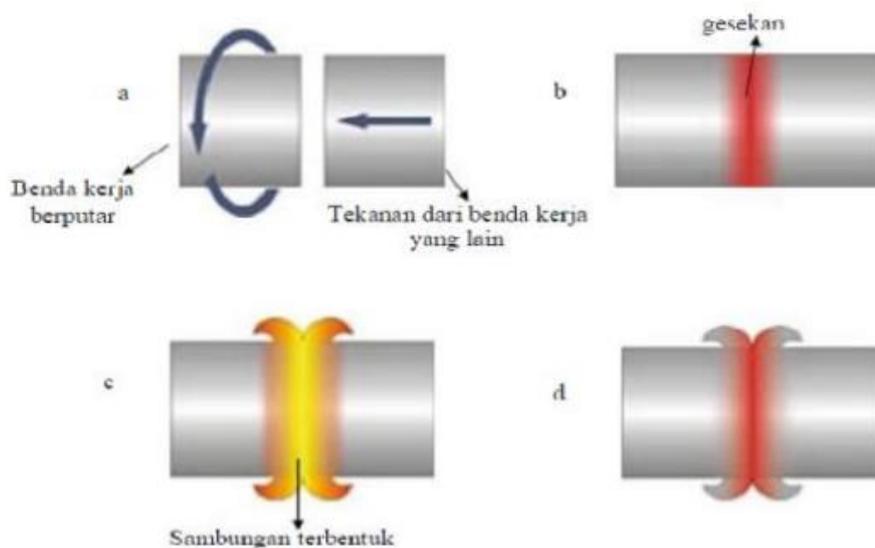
Prinsip *friction stir welding* (Endartyana,2013)
